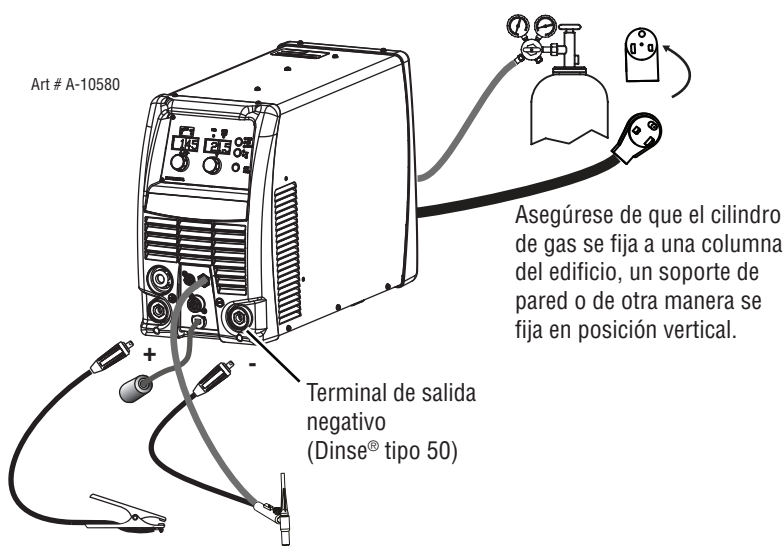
Configuración de la soldadura LIFT TIG (GTAW)
